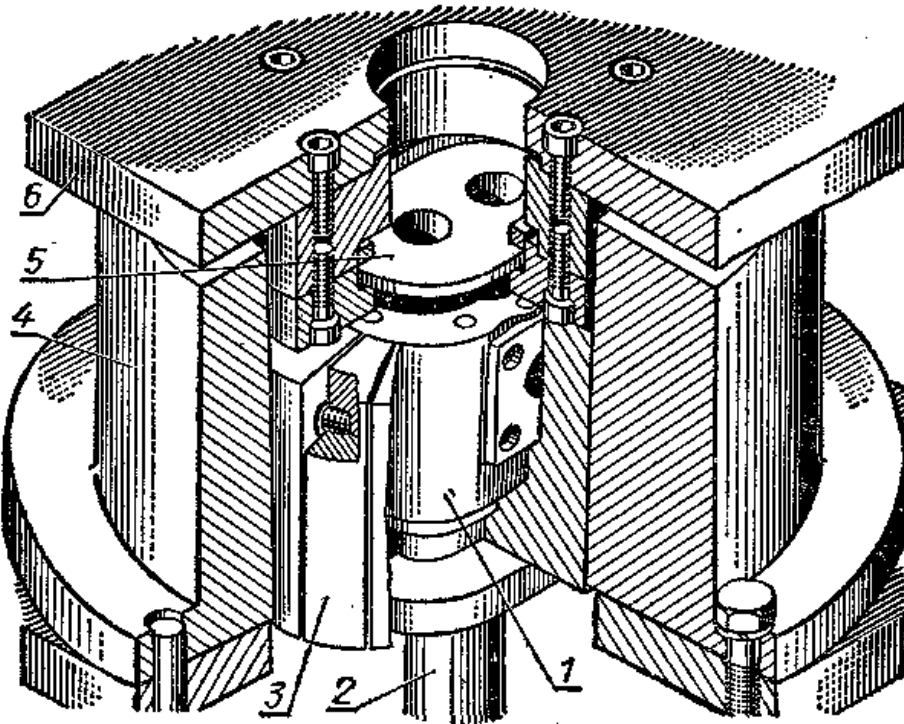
Пристосування для обтиснення корпусу насоса а процесі гарячого пластичного деформування:
